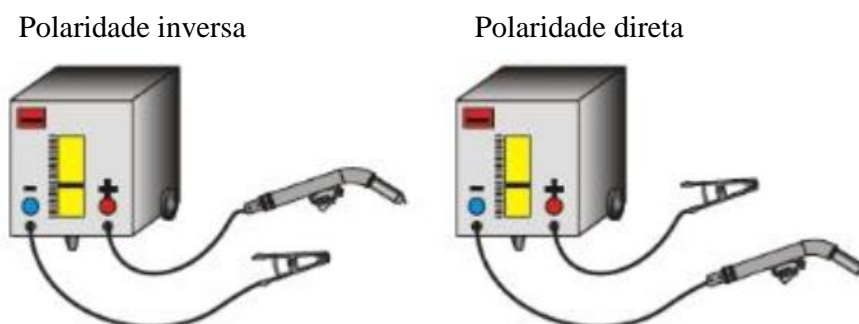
Tipo de polaridade utilizada na soldagem GMAW.
